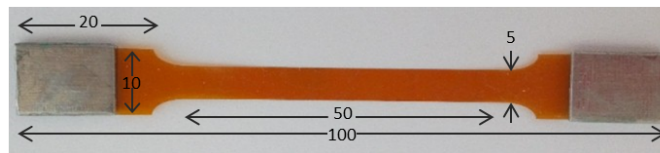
Éprouvette de traction (dimensions en mm).
